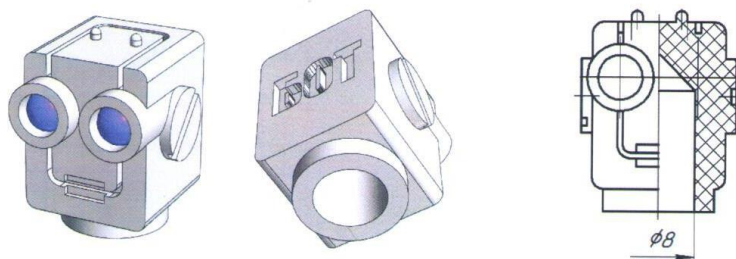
Образец изделия «Колпачок» и его профильный вид с местным разрезом
